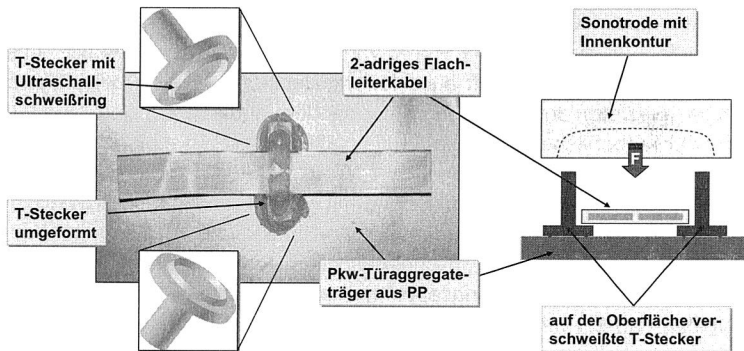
Fixierung von Flachkabeln durch Ultraschallumformung aufgeschweißter T-Stecker (nach [102])
